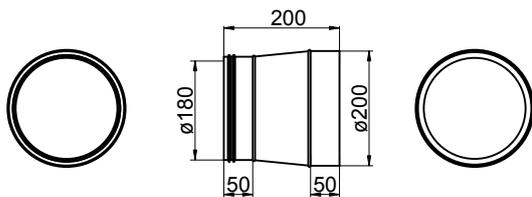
Dimensions de raccord de transition DN180 (dimensions en mm)
